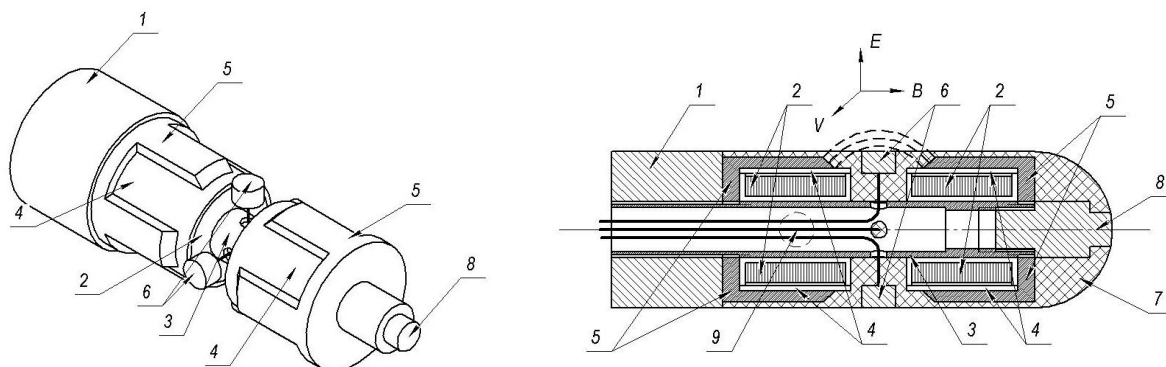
Общий вид конструкции преобразователя и его продольный разрез
